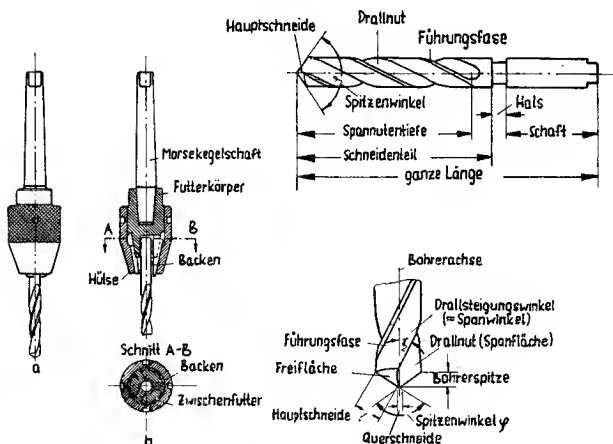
Bohrwerkzeuge; links Dreibocken-Bohrfutter mit konischem Schaft, rechts oben Spiralbohrer mit Bezeichnung der Einzelheiten und rechts unten die Bohrerspitze mit den entsprechenden Winkeln
